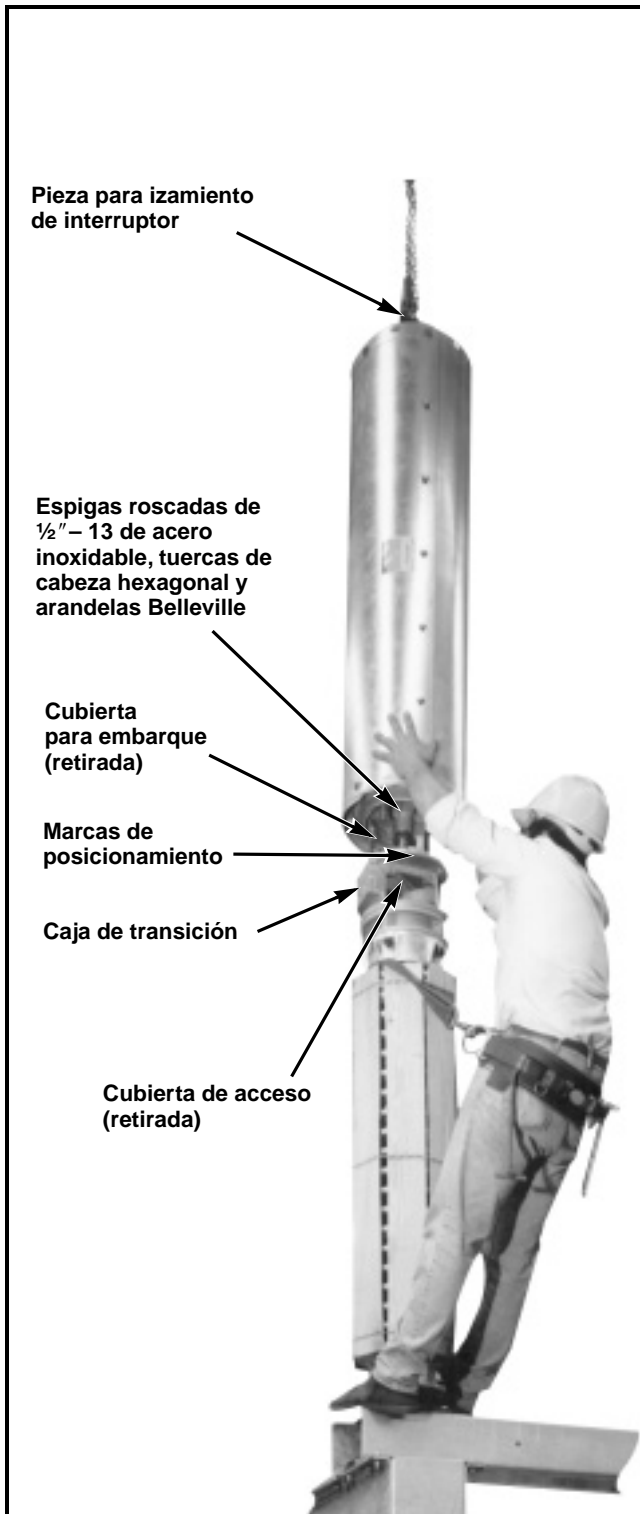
Ensamblaje del interruptor a la columna aislante soporte.
